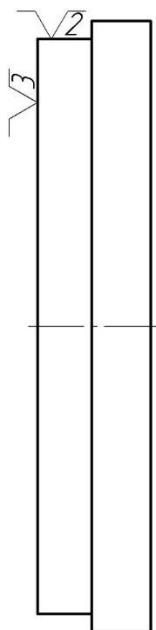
Схема базирования заготовки типа диск в трехкулачковом самоцентрирующемся патроне
